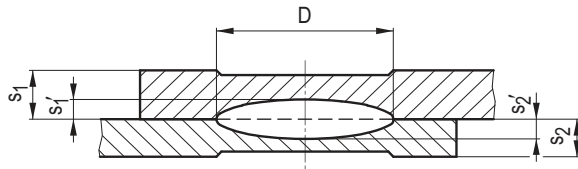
Abmessung für Schweißlinse und Eindringtiefe der Elektroden bei Punktschweißungen
